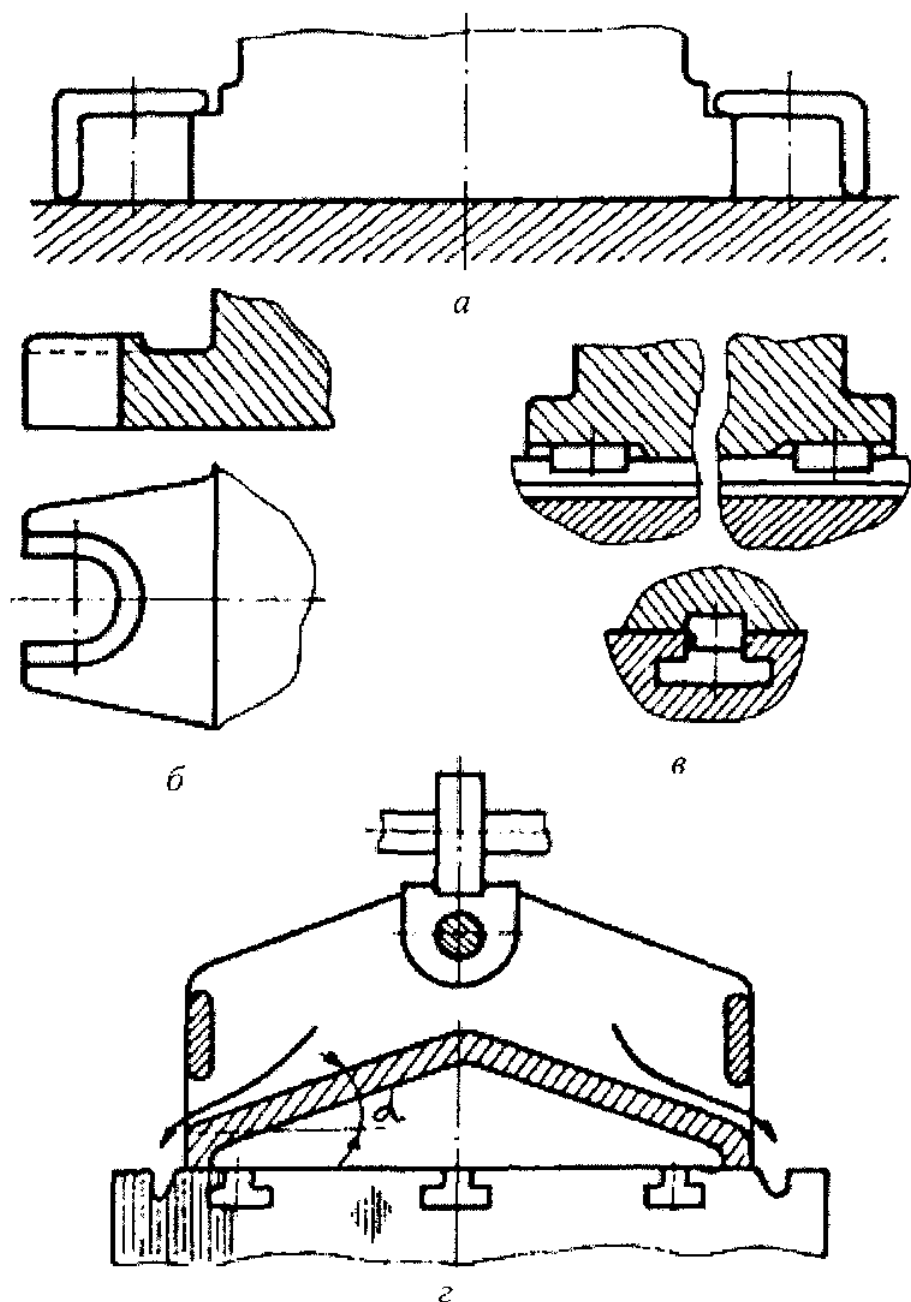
Варіанти закріплення корпусу на столі верстата (а-б) і схема корпусу пристрою з відведенням МОР і стружки (з)
